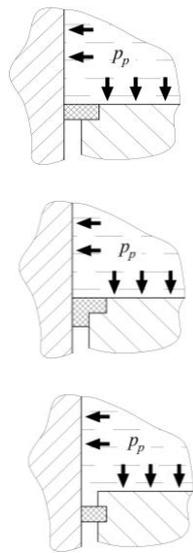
Варианты уплотнительных соединений с упорными кольцами
